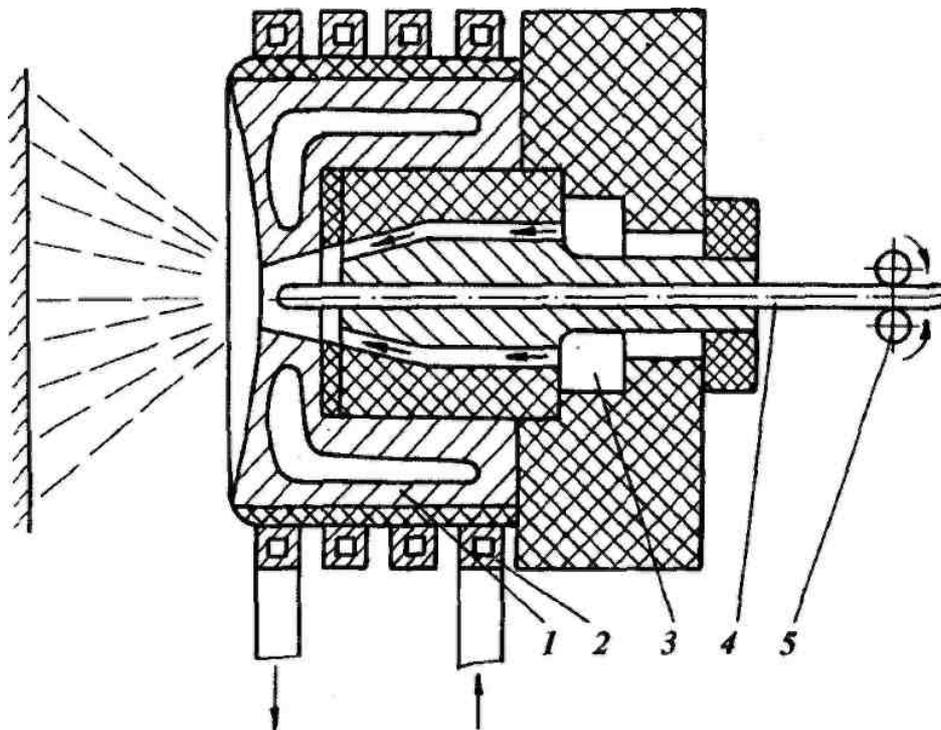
Устройство для индукционного напыления: 1 – концентратор тока; 2 – индуктор; 3 – воздушный канал; 4 – проволока; 5 – подающие ролики
